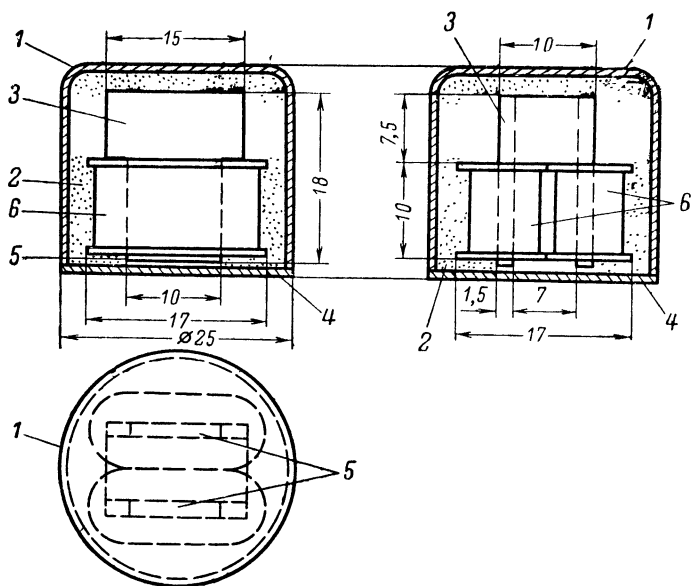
Электромагнитный звукосниматель для преобразования колебаний корпуса инструмента.
